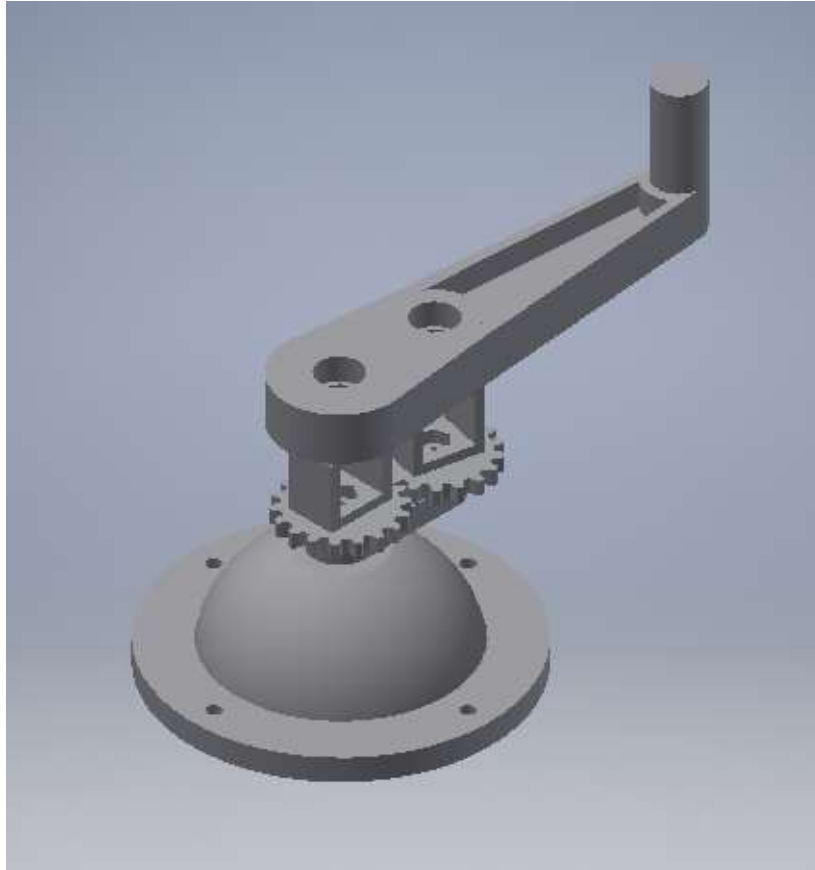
Vista isométrica del ensamblaje del V.I.M. Rotor-Estator.
